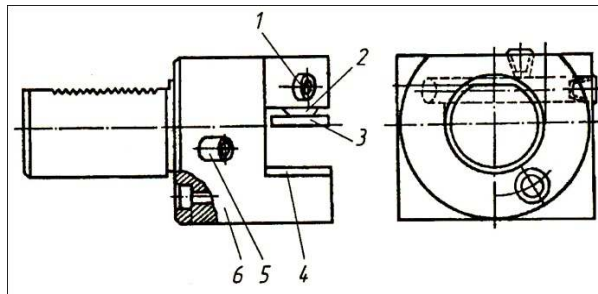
Резцедержатель с цилиндрическим хвостовиком к станам токарной группы
